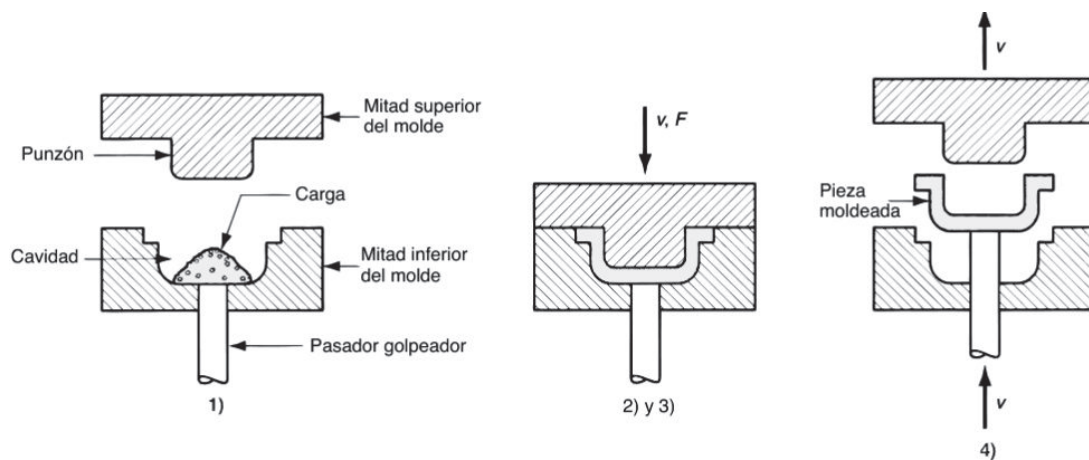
Moldeo por compresión: 1) carga del material; 2) y 3) compresión y fundido; 4) retirado de la pieza.
